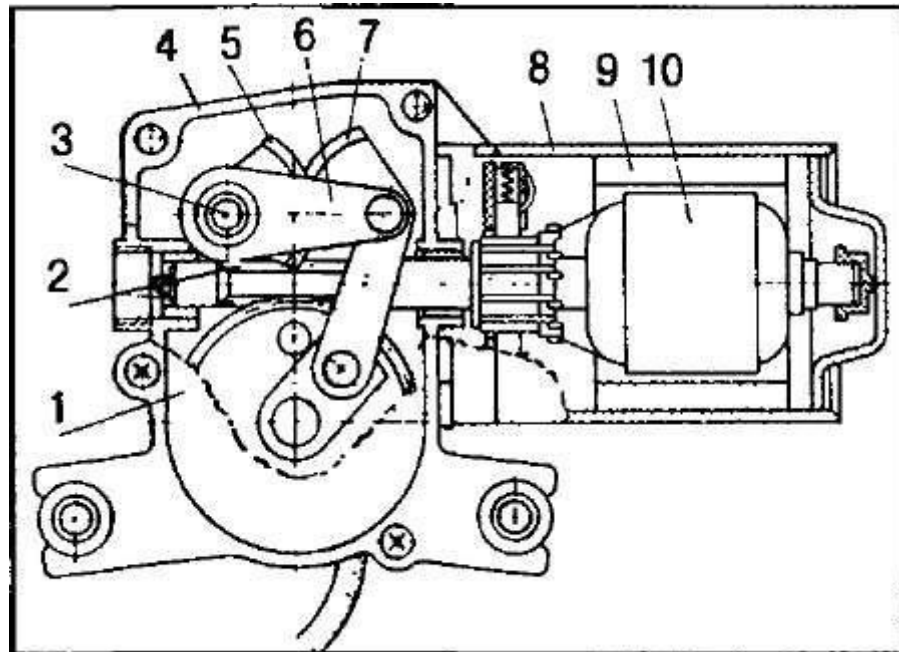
Моторедуктор склоочисника заднього скла.(1 – шестерня; 2 – черв'як; 3 – вихідний вал; 4 – корпус редуктора; 5, 7 – зубчасті сектора; 6 – сережка; 8 – корпус електродвигуна; 9 – постійний магніт; 10 – якор.)
